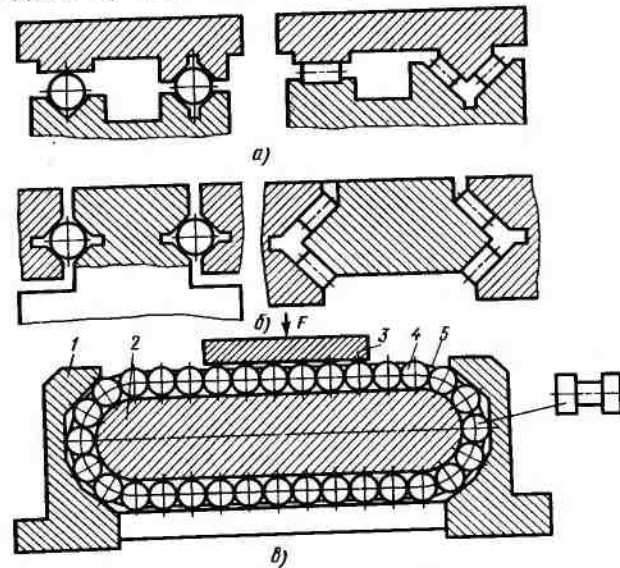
Направляющие качения: а) — открытие, б) — закрытие, а — роликовые; 1 — опора, 2 — направляющая, 3 — исполнительный орган станка, 4 — ролики, 5 — сепаратор
